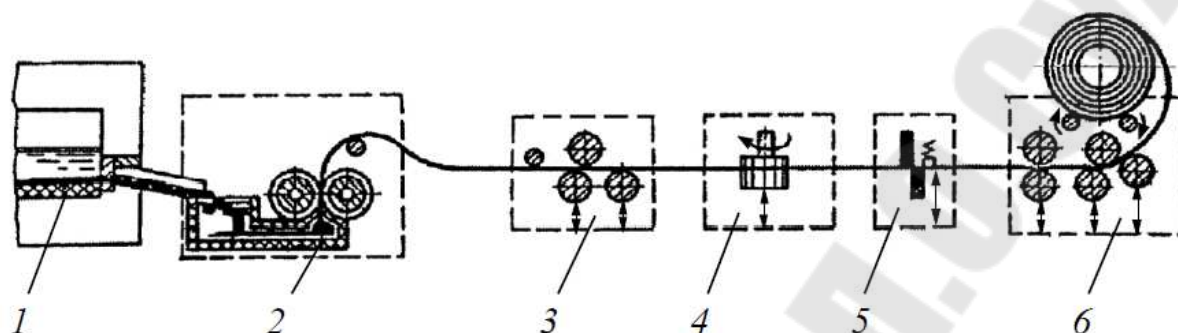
Литейно-прокатный агрегат для производства алюминиевой полосы: 1 – миксер; 2 – валковый кристаллизатор; 3 – правильная машина; 4 – машина для фрезерования боковых кромок; 5 – ножницы; 6 – свертывающая машина
